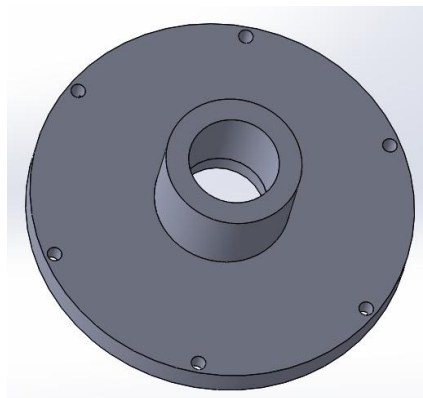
Vue en perspective du couvercle de la chambre.
